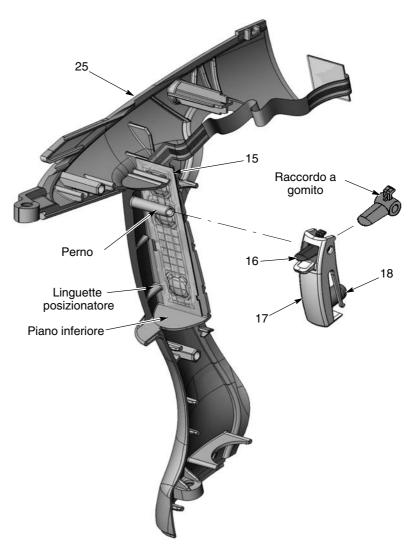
Montaggio dell'interruttore grilletto e del grilletto
